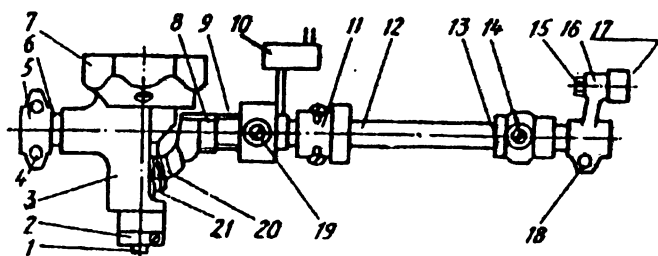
Механизм корпуса хода челнока, вала и кривошипа (машина «Подольск» 142 кл.):
